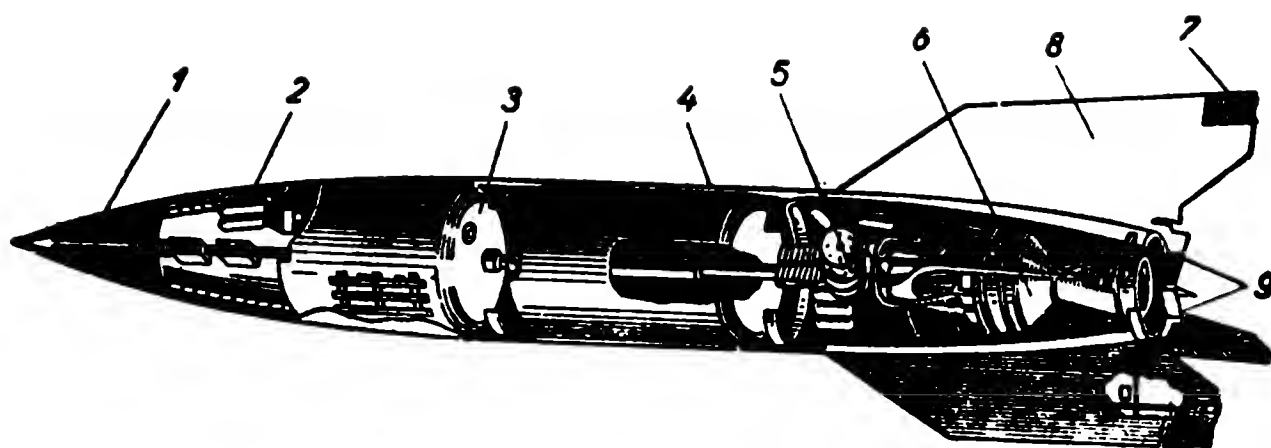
Схема устройства баллистической ракеты ФАУ-2: 1 — боевой заряд; 2 — приборы управления; 3 — бак с горючим (спирт); 4 — бак с окислителем (жидкий кислород); 5 — насосы питания двигателя; 6 — жидкостный реактивный двигатель; 7 — воздушные рули управления; 8 — плоскость стабилизатора; 9 — газовые рули за соплом двигателя
